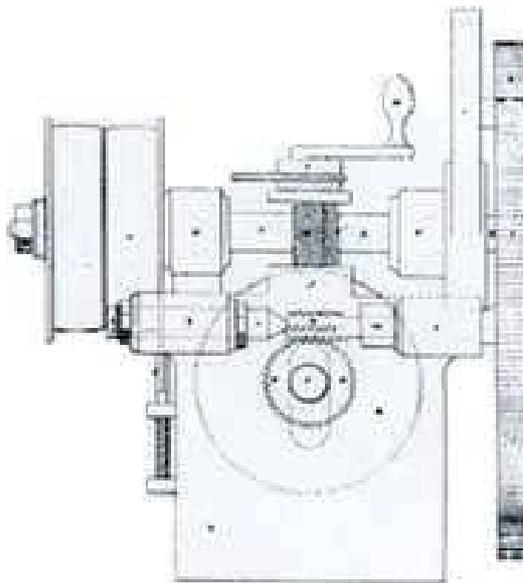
Máquina generadora de engranes patentada por Joseph Whitworth en 1835
